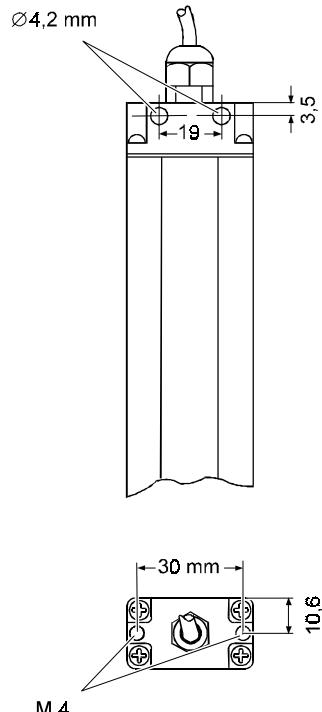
Befestigungsbohrungen in den Profilendstücken
